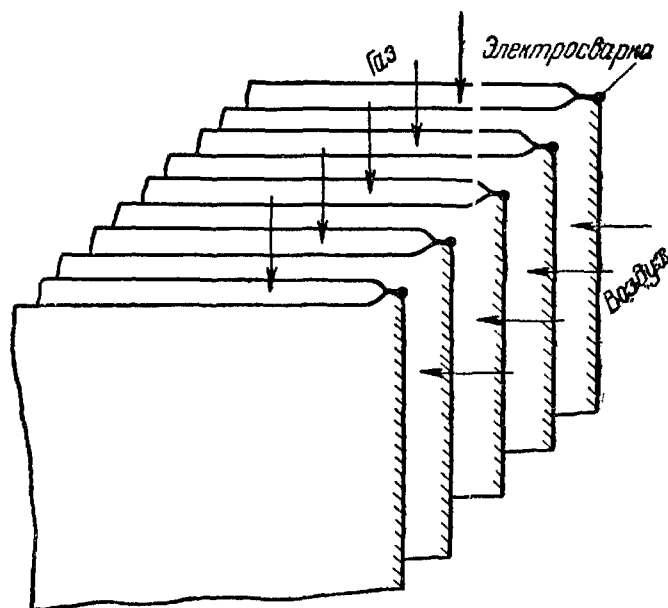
Схематическое устройство пластинчатого воздухоподогревателя.
